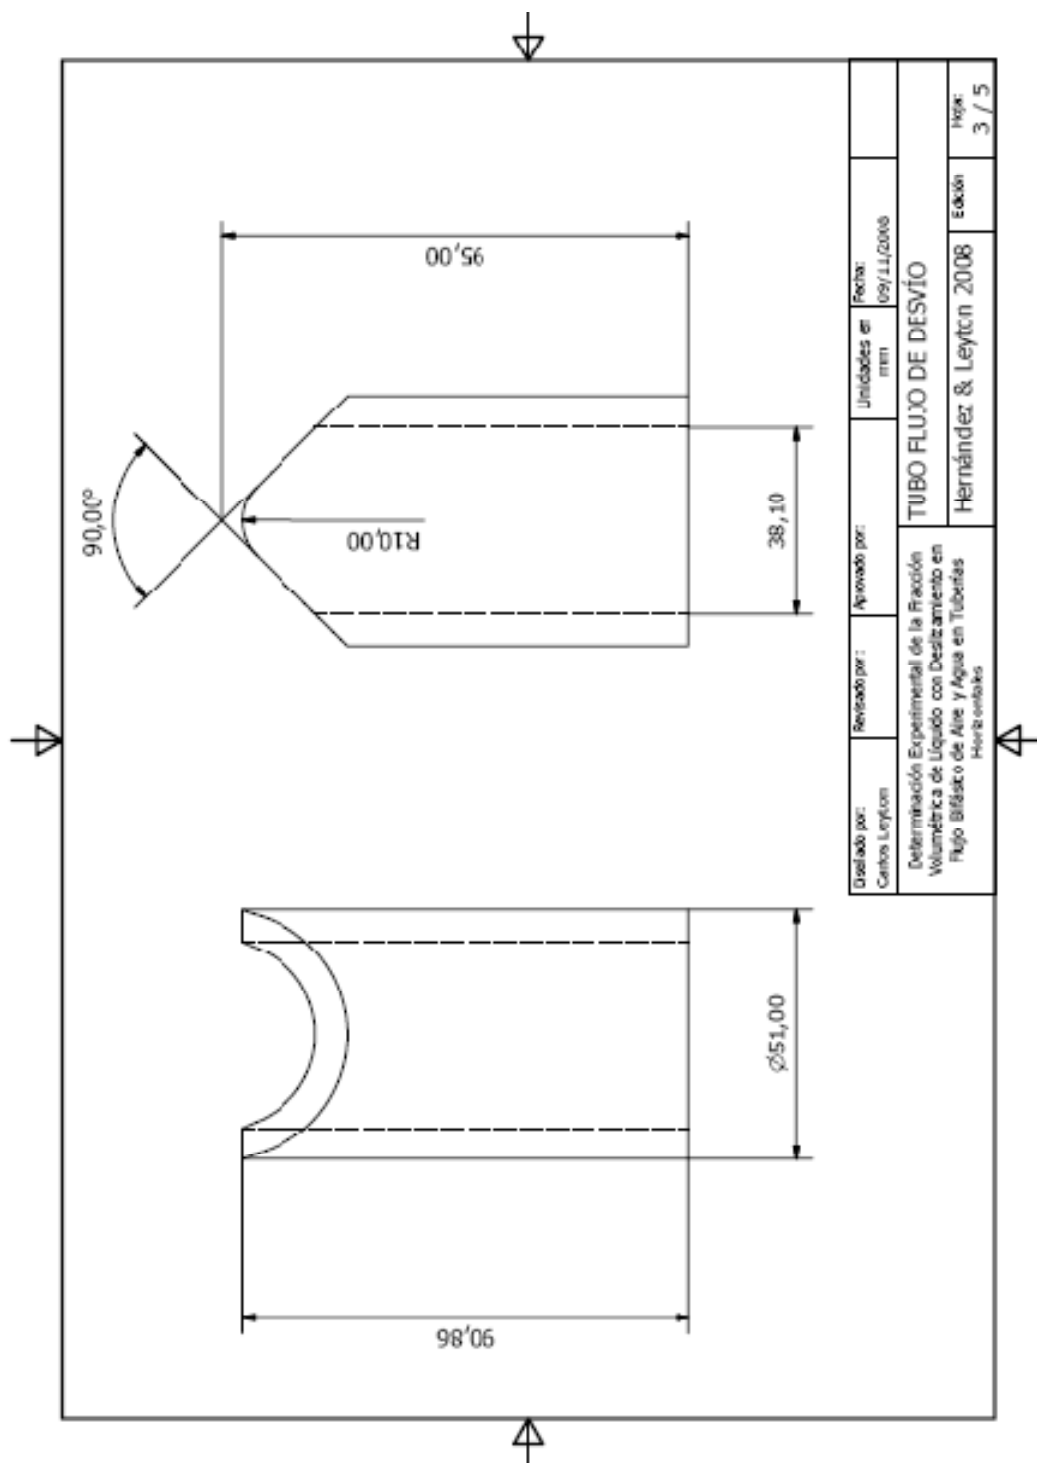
Planos constructivos de la Sección de desvío de flujo (3/5).
